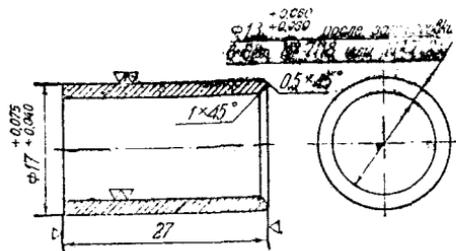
Дет. № 7119. Втулка фланца и корпуса подкачивающей помпы
